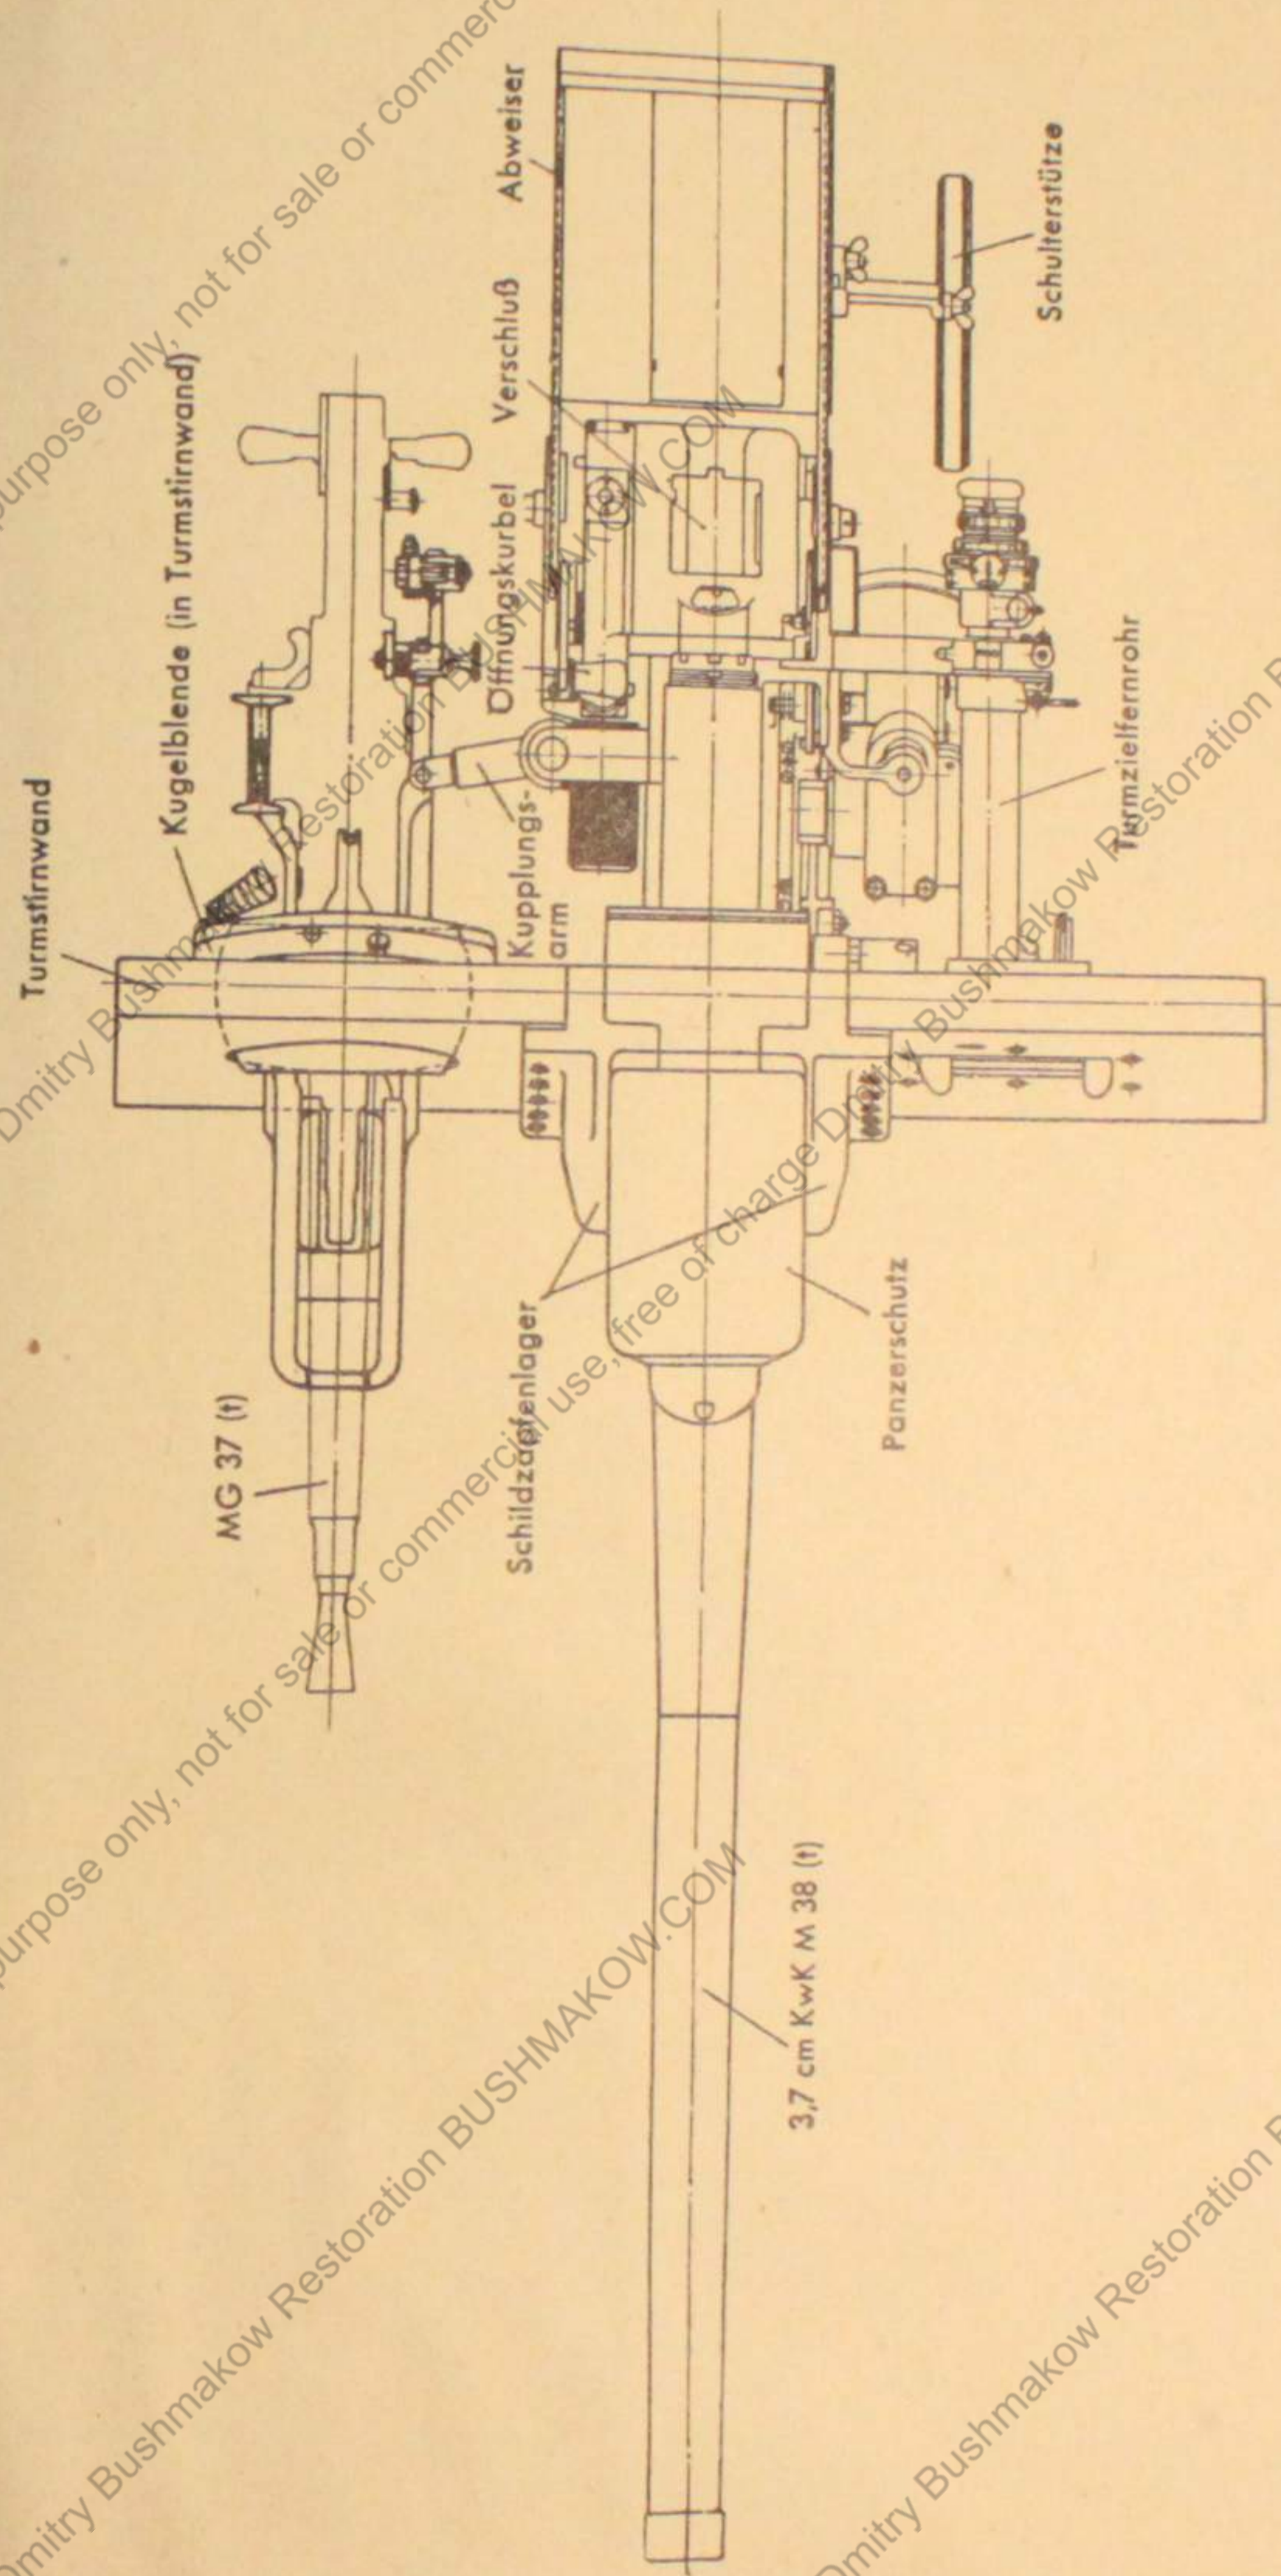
Waffenlagerung 3,7 cm KwK M 38 (t) und MG 37 (t), Grundriss
